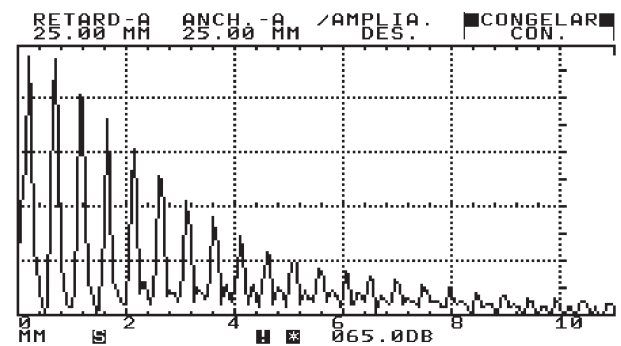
Oscilograma de ultrasonidos de una falta de soldadura.
